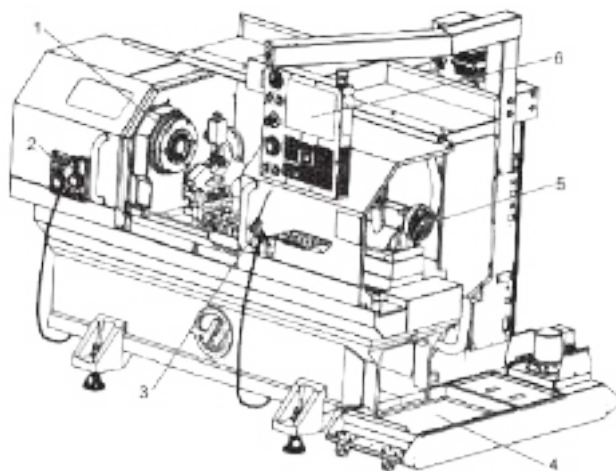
Токарний верстат серії Toolroom (Haas) (вигляд спереду): 1 — вузол шпинделя; 2 — електронний маховичок; 3 — пістолет для продування; 4 — резервуар МОР; 5 — задня бабка; 6 — підвісний пульт керування
